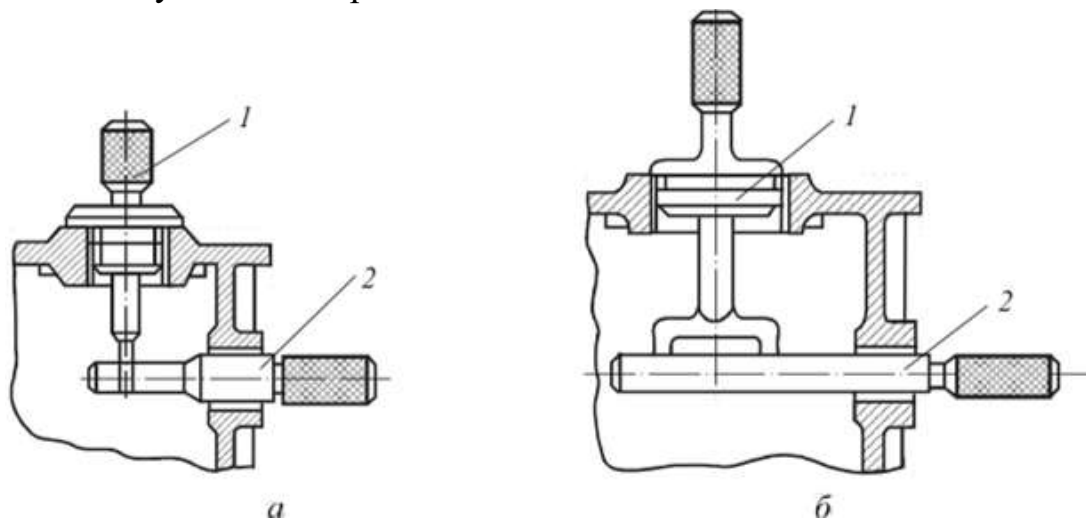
Схема контролю розташування осей у корпусі конічного редуктора
